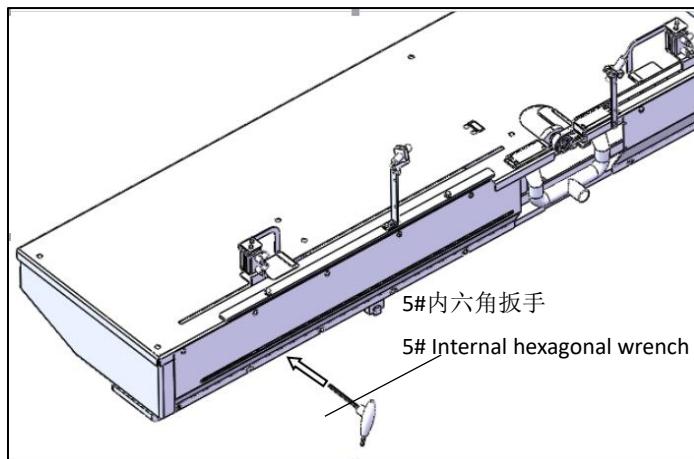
移料机构图 Figure 7.1 Feeding MechanismDrawing
